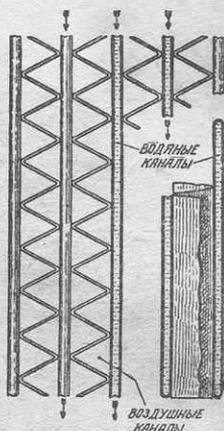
а. Пластиначный радиатор с прямыми лентами и зигзагообразными жестяными листами.
